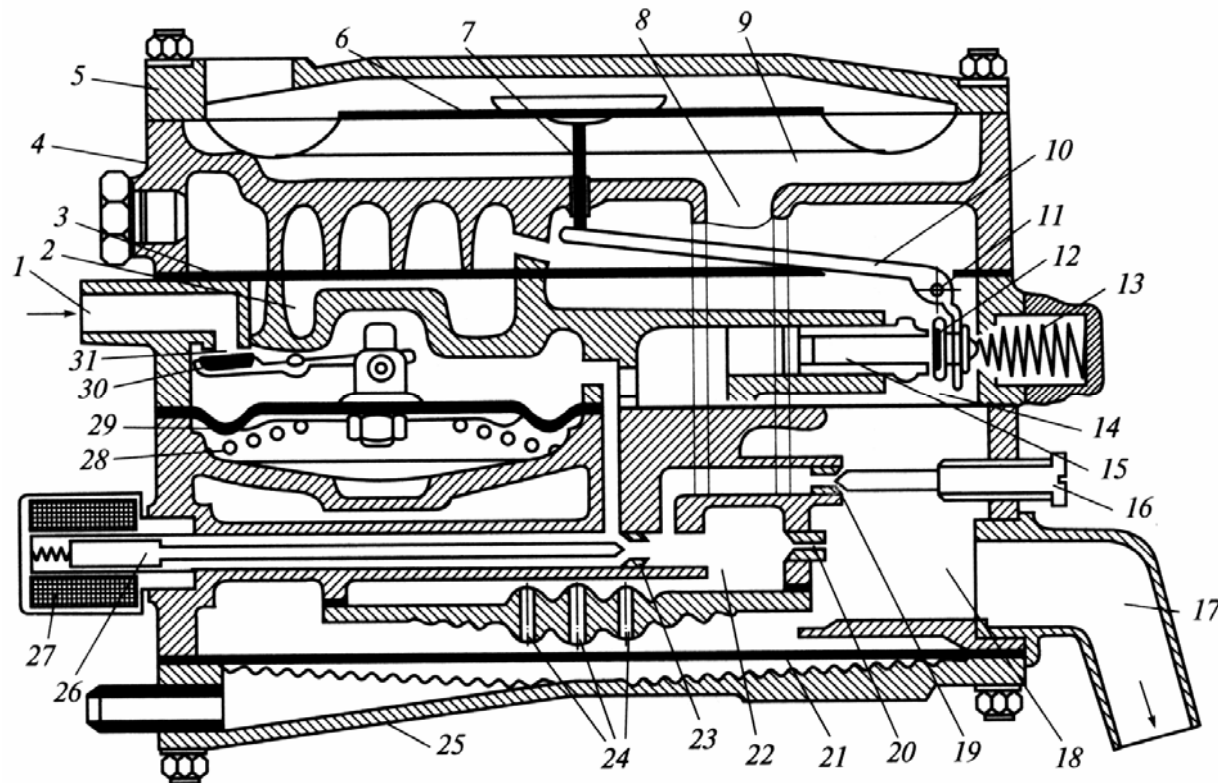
Схема редуктора низкого давления РЗЗА:
